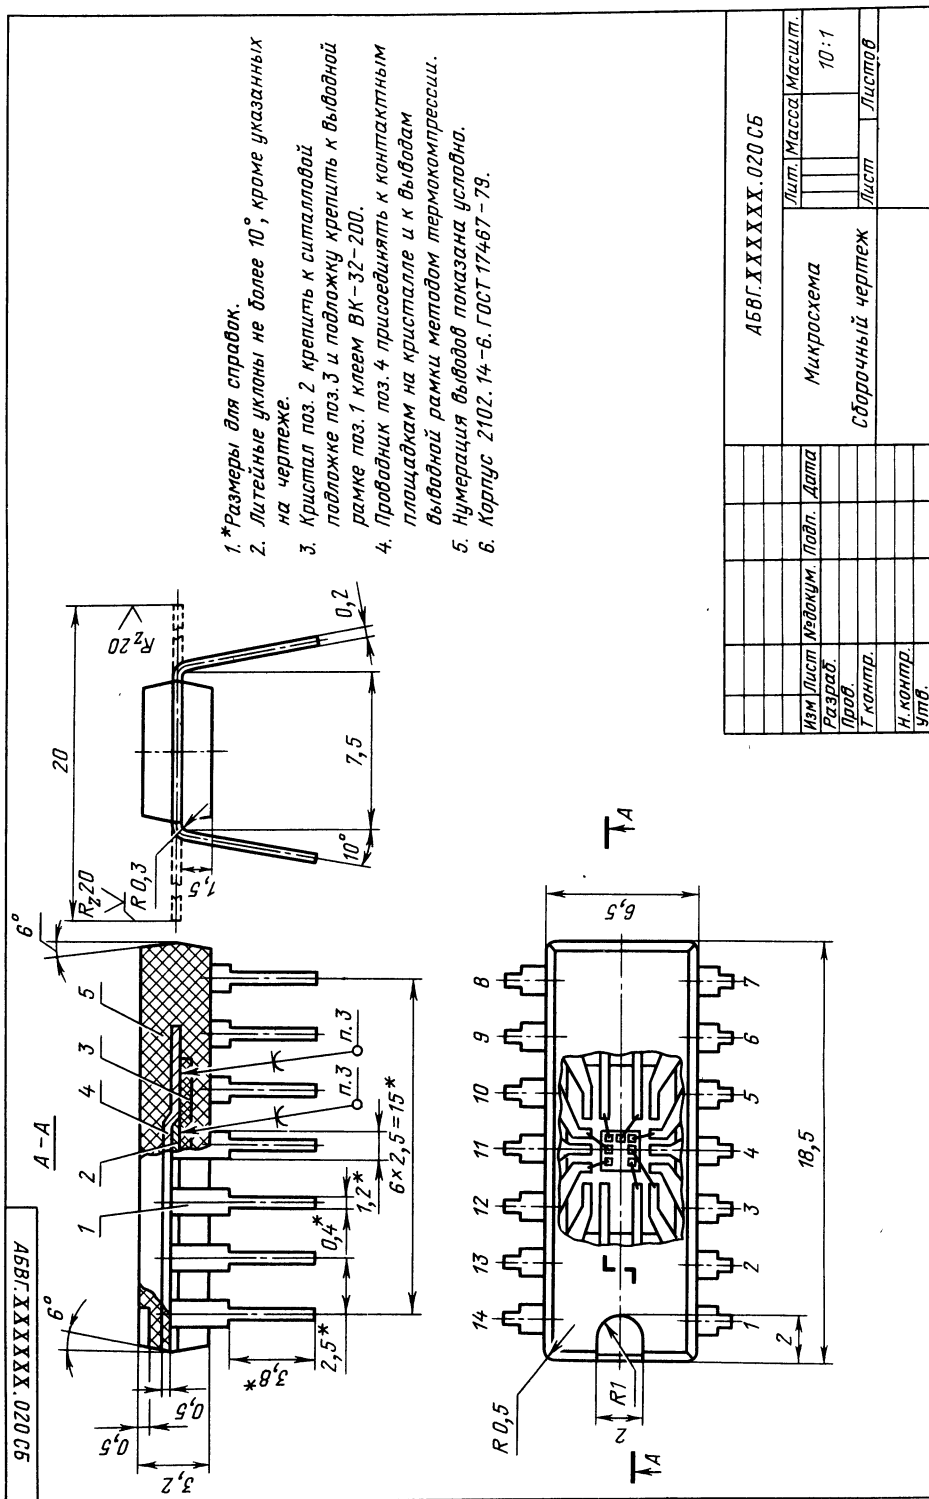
Сборочный чертеж полупроводниковой ИС
